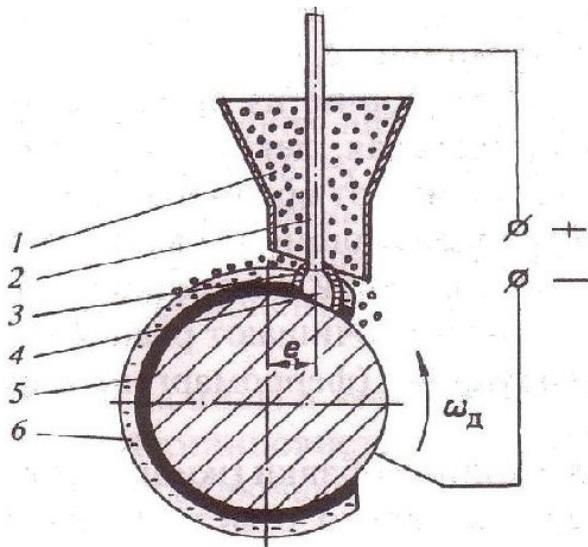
Наплавка цилиндрической детали под слоем флюса:
